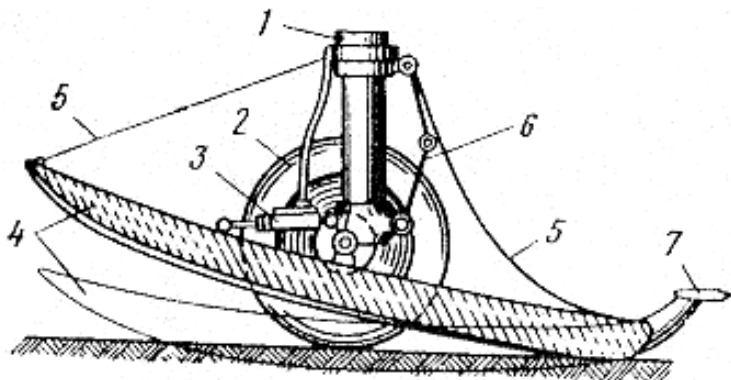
Конструктивная схема колесно-лыжного шасси.
